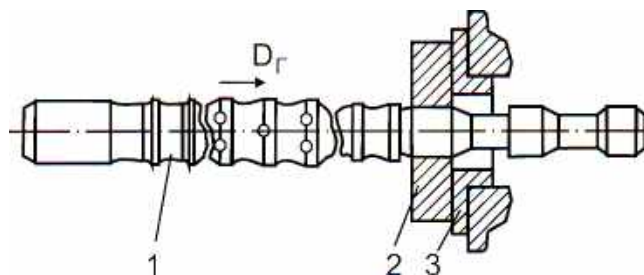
Схема оброблення поверхні на протяжних верстатах
